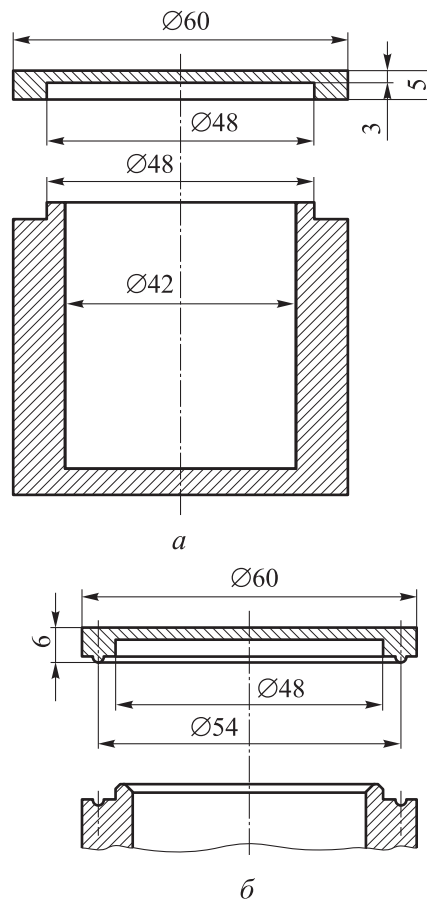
Схемы изделия круглого сечения: а — стакана и крышки; б — V-образной разделки крышки, стакана и оптимального варианта разделки при сварке стакана с крышкой
